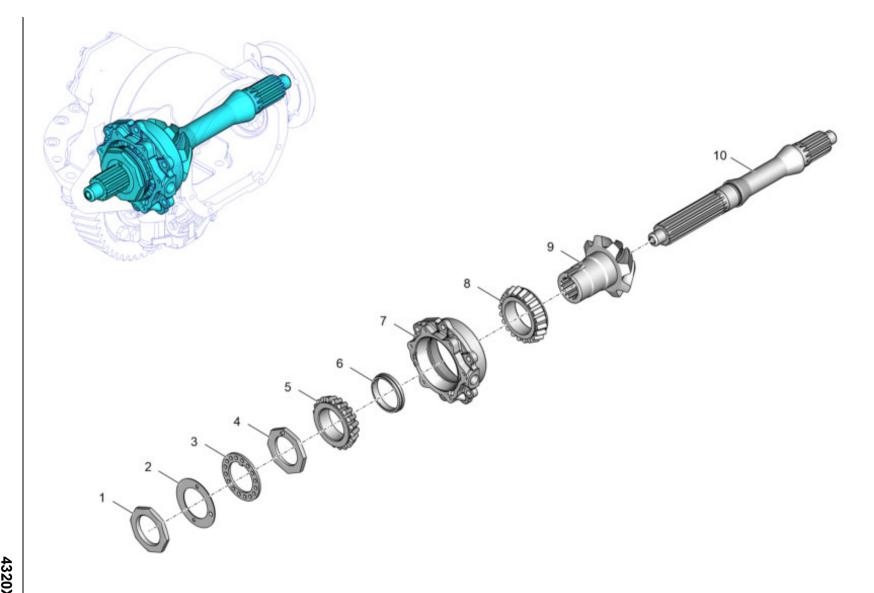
4320X-2502005 Установка ведущей конической шестерни
